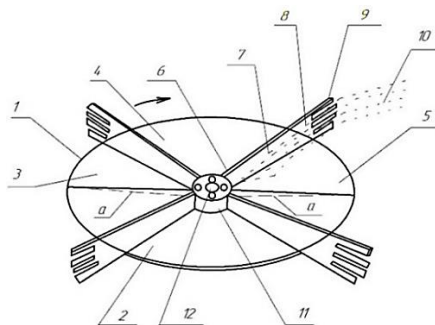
Дисковый рабочий орган для разбрасывания твердых органоминеральных удобрений: 1 – диск; 2, 3, 4, 5 – сектор; 6 – лопатка; 7 – центральная часть лопатки; 8 – выходная часть лопатки; 9 – пластина; 10 – гранулы; 11 – ступица; 12 – вал
